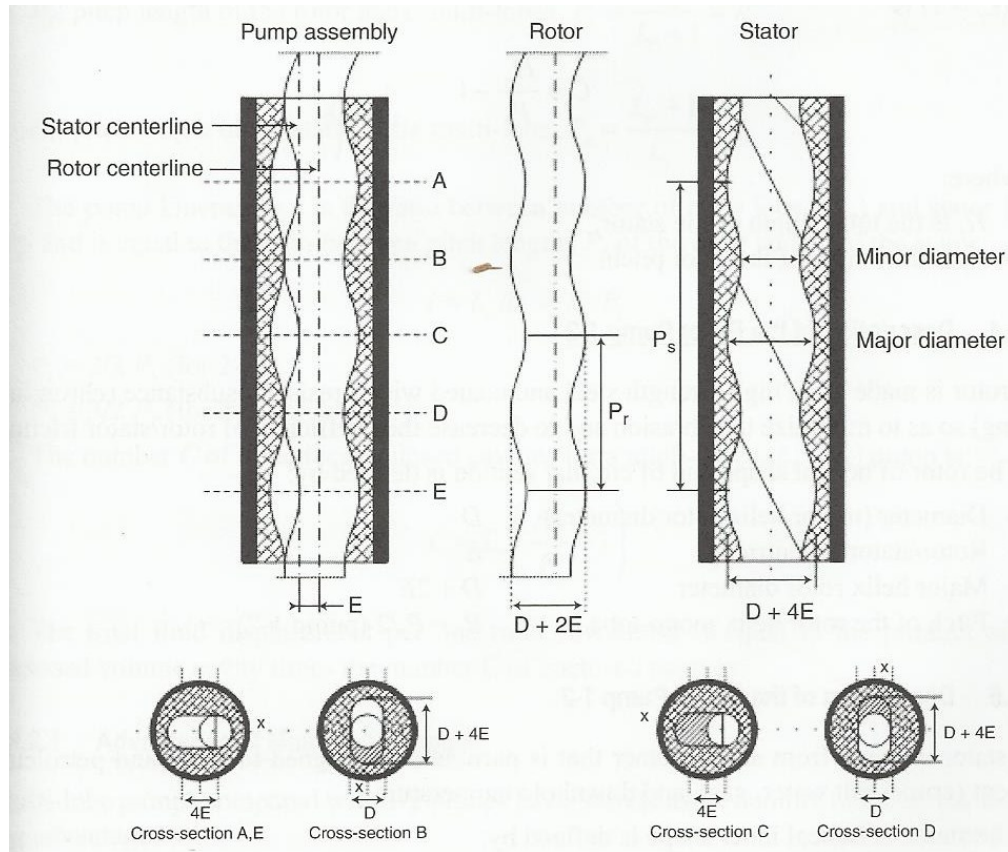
Geometria de Bomba 1-2 - Rotor e estator [6].
